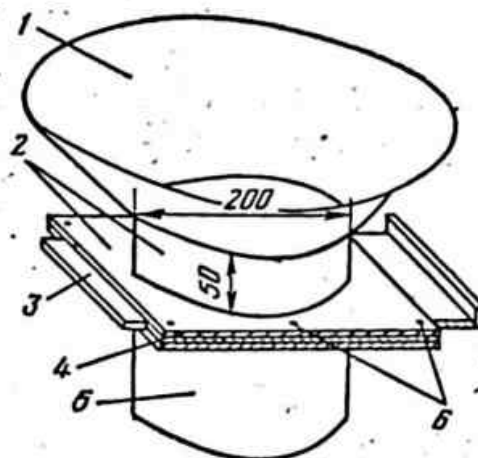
Разгрузочный шибер: 1 — конус бункера; 2 — корпус шибера; 3 — заслонка; 4 — прокладка; 5 — зернопровод разгрузочный; 6 — болты крепления.
